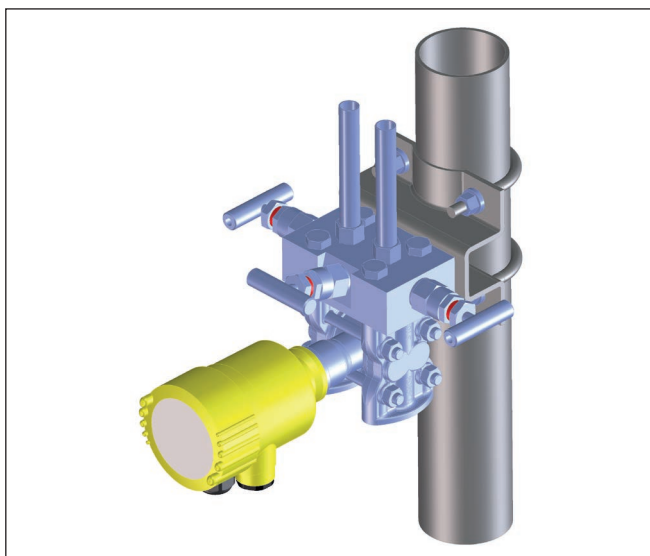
Esempio di montaggio di un supporto universale per gruppi di valvole
